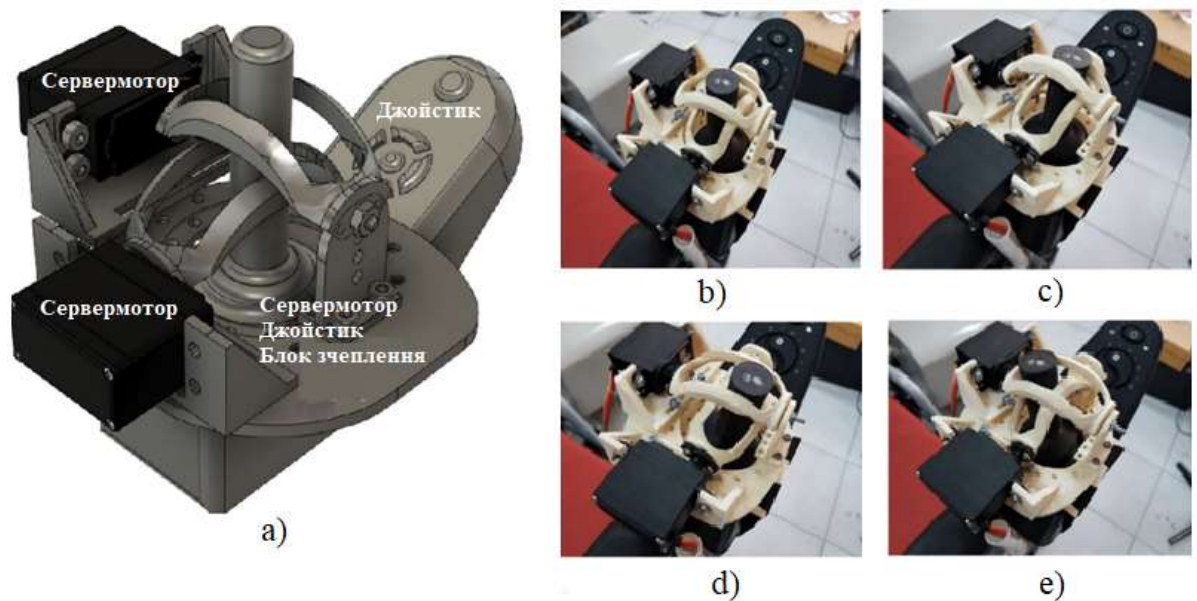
Блок з'єднання сервомотора джойстика: (а) конструкція; (б) зупинка; (с) вперед; (д) поворот праворуч; (е) робота повороту ліворуч
